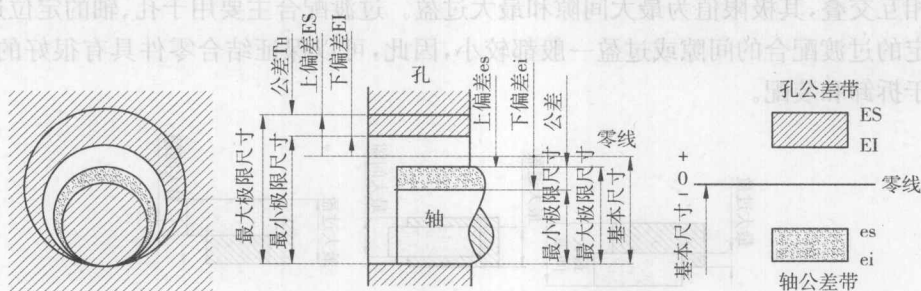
尺寸偏差、公差及公差带示意图
